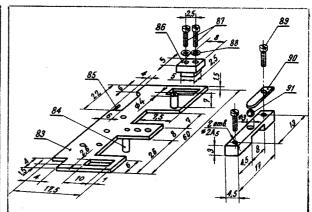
Планка магнитных головок и прижимного ролика: 83 - планка, Д16-T; 84 - стойка \varnothing $3 \times \times 7$ мм, Ст. 45; 85 - штифт $1\Gamma \times 5$ мм; 86 - направляющая, Л62-T; 87 - винты $M1,4 \times 6$, 4 шт.: 88 — шайба; 89 — винт М2×5, 2 шт.; 90 — пружина фиксатора, Ст. 60С2А; 91 — шарик стальной диаметром 3 мм.
